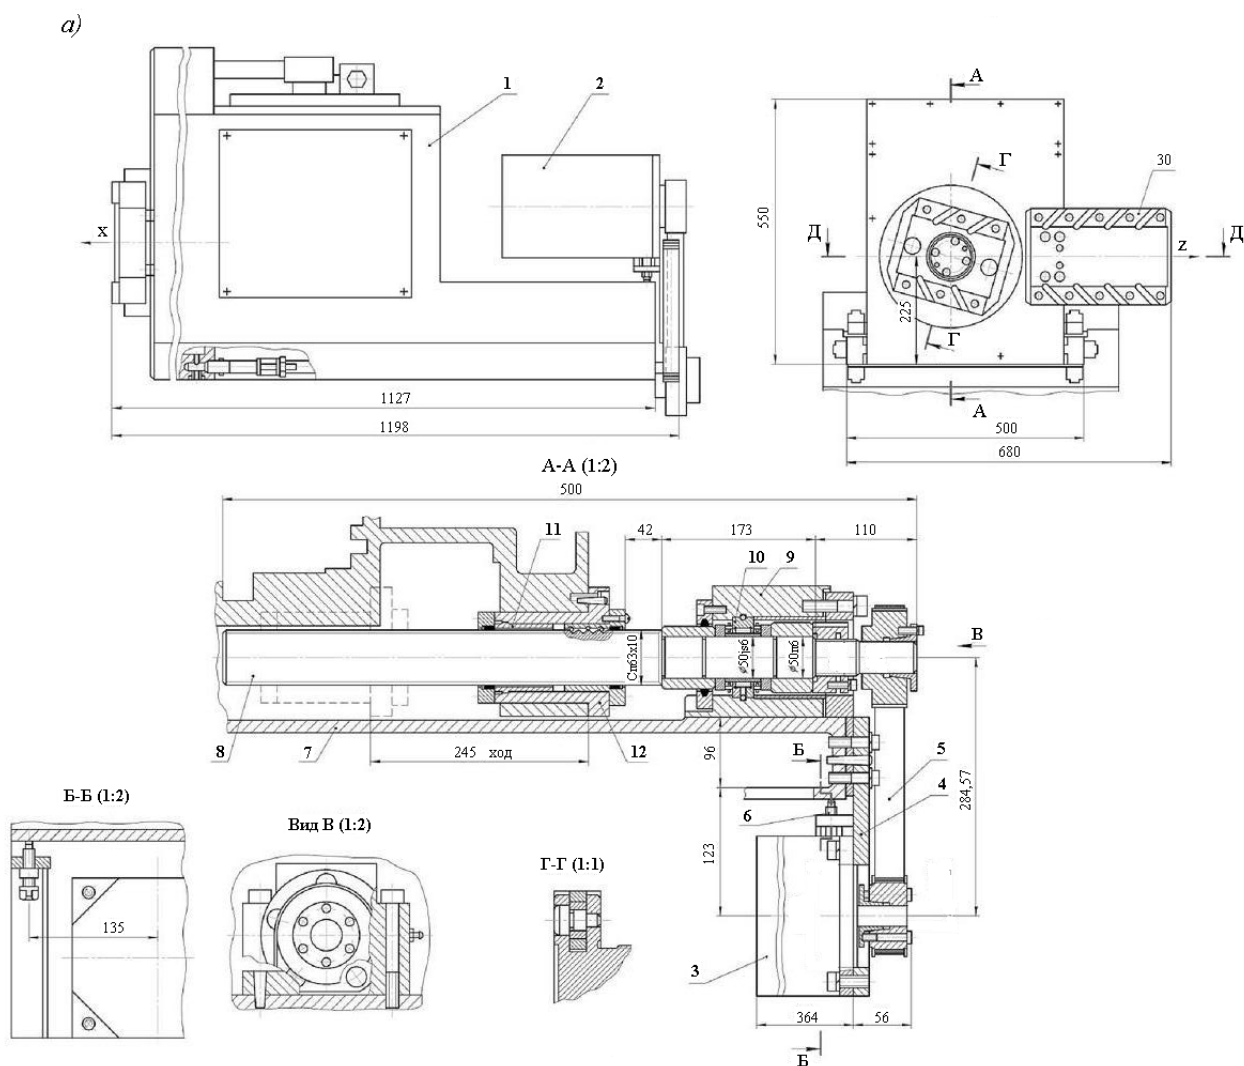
а. Общий вид механизма поперечно-подвижного суппорта и револьверной головки станка ИРТ180ПМФ4
